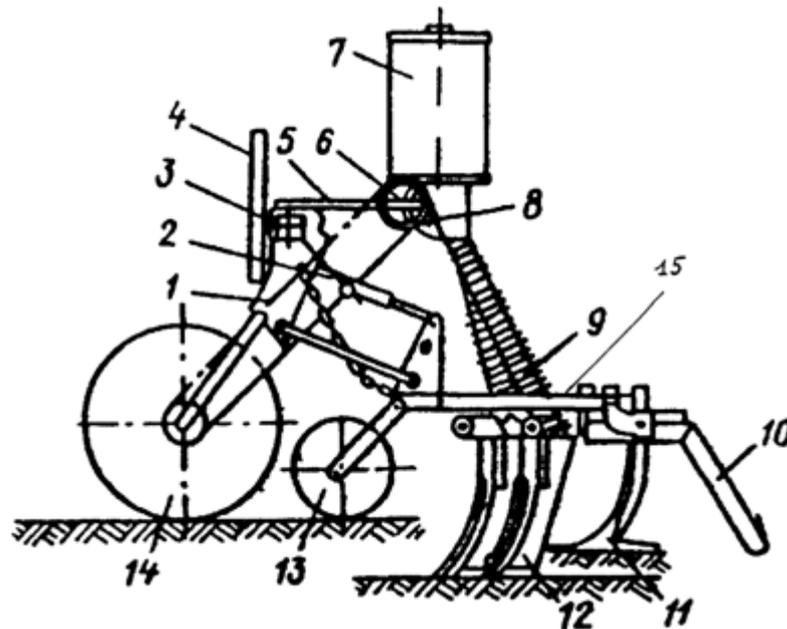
Универсальная свекловичная машина - культиватор УСМК - 5,4: 1 - приводная цепь; 2 - натяжной ролик; 3 - брус; 4 - замок автосцепки; 5 - кронштейн туковысевающего аппарата; 6 - соединительный валик; 7 - туковысевающий аппарат; 8 - звездочка; 9 - тукопровод; 10 - подножная площадка; 11 - стрельчатая лапа; 12 - подкормочный нож; 13 - копирующее колесо секции рабочих органов; 14 - опорное колесо бруса; 15 - грядиль.
